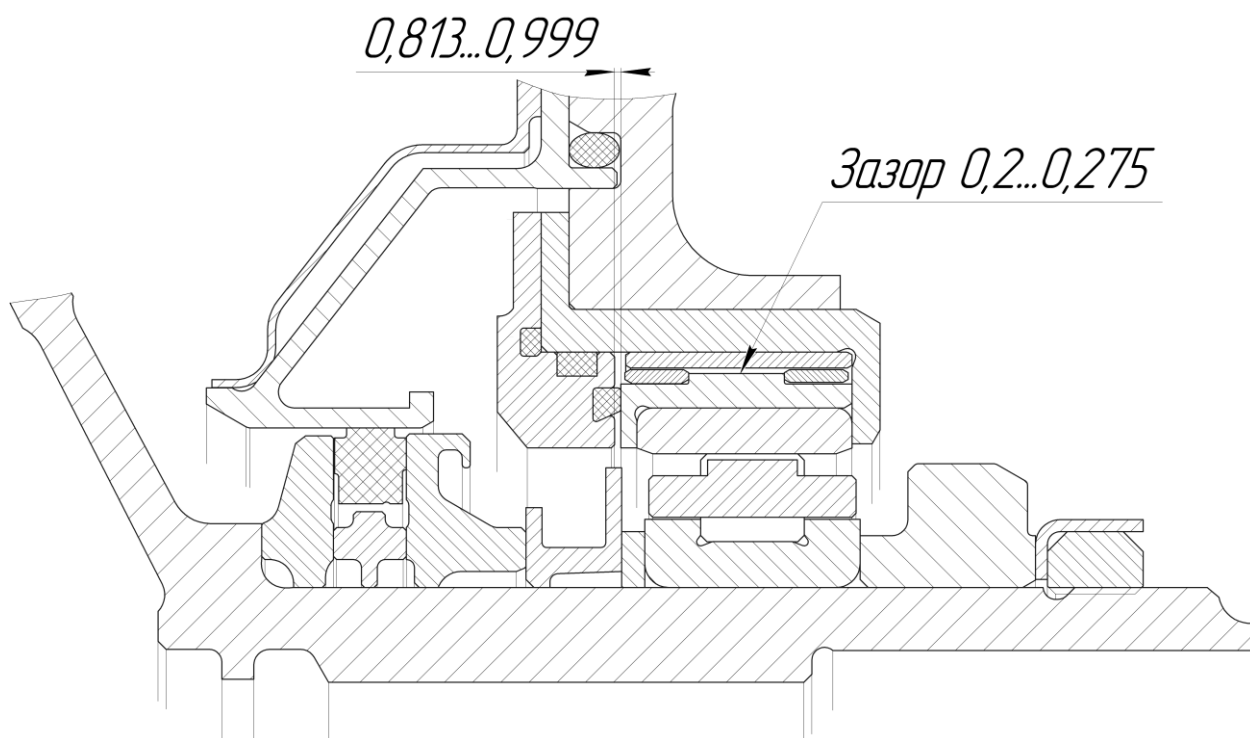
Подшипниковый узел с проведёнными мероприятиями
